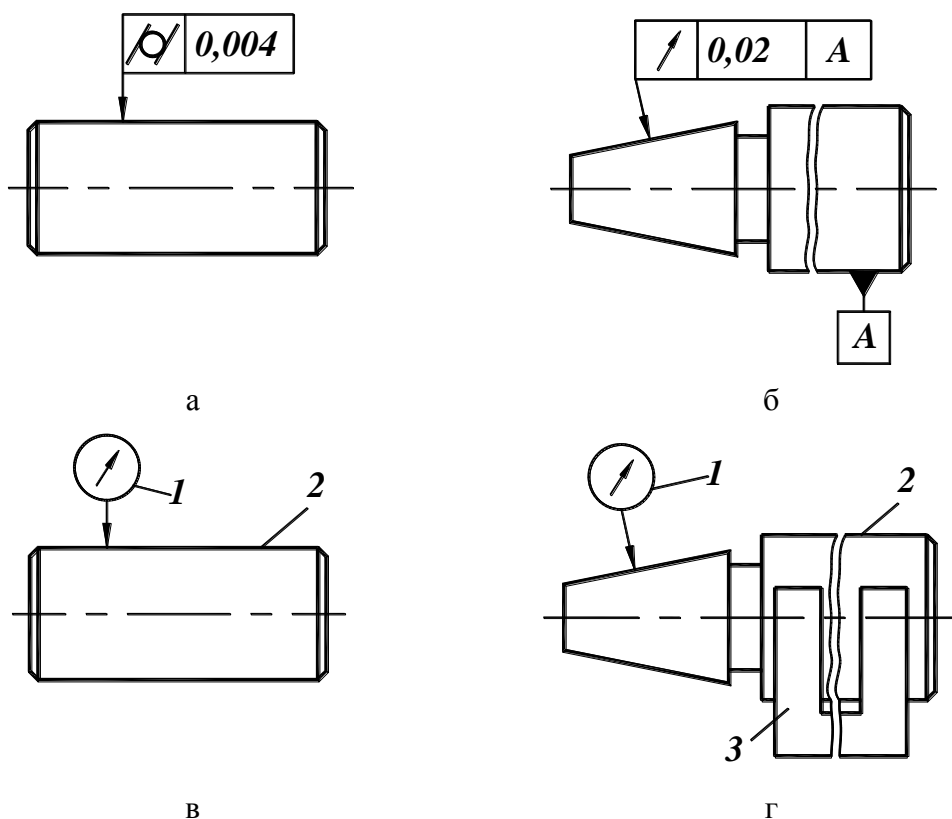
Примеры указания на чертежах и схемах измерений направления линии измерений: а, б– условное обозначение на чертежах деталей допусков цилиндричности и биения в заданном направлении; в, г– схемы измерения соответствующих отклонений
